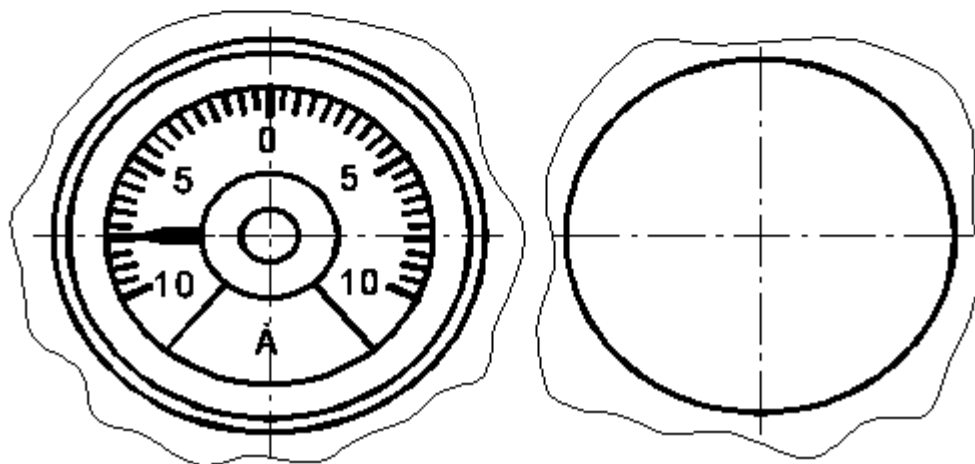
Габаритный чертеж прибора М1611.2-2
